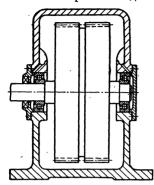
Циркуляционная смазка подшипника (смазка собирается Vобразными канавками)
